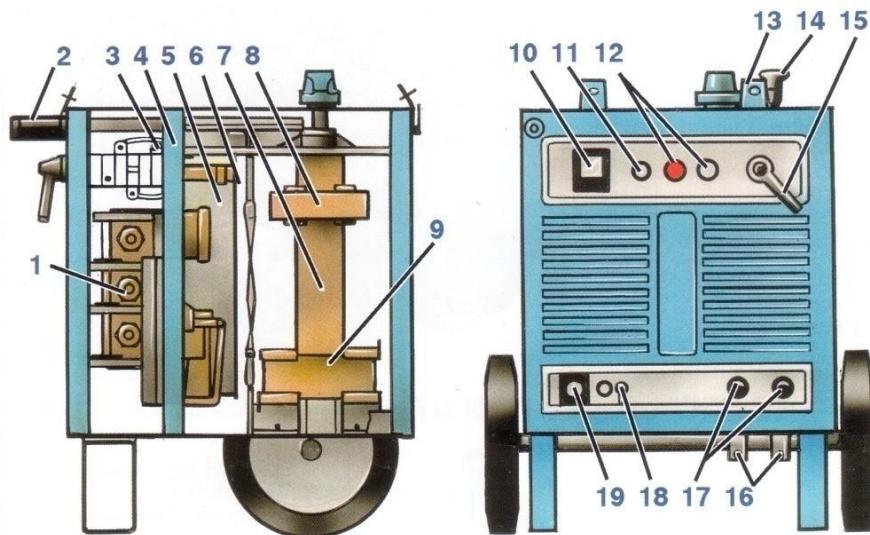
Внешний вид и основные сборочные единицы и детали сварочного выпрямителя: 1 – выпрямительный блок; 2 – выдвижные ручки; 3 – предохранители; 4 – блок аппаратуры; 5 – вентилятор; 6 – реле ветровое; 7 – трансформатор силовой; 8 – вторичная обмотка; 9 – первичная обмотка; 10 – амперметр; 11 – лампа; 12 – кнопки управления; 13- скобы; 14 - рукоятка регулирования тока; 15 – переключатель диапазона тока; 16 – шины заземления обратного провода; 17 – токовые разъёмы; 18 – болт заземления; 19 – штепсельный разъём для подключения к сети
